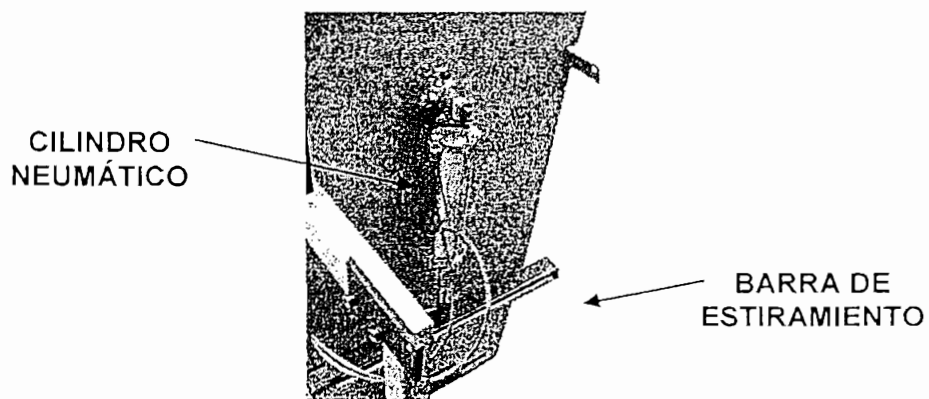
Conjunto para desenrollar la lámina de polietileno
